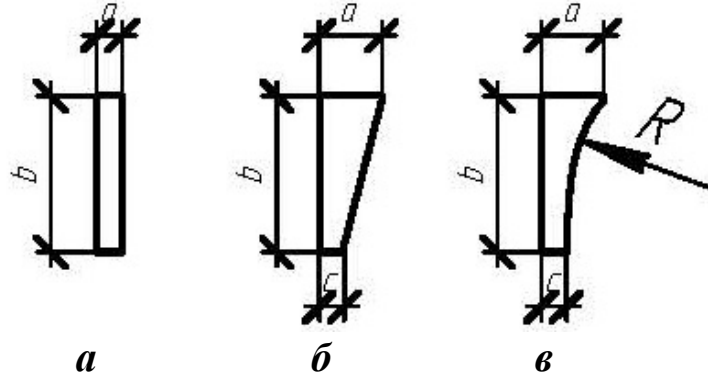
Формы сопла дождевальной насадки: *a* – прямоугольная; *б* – трапецевидная; *в* – переменная
